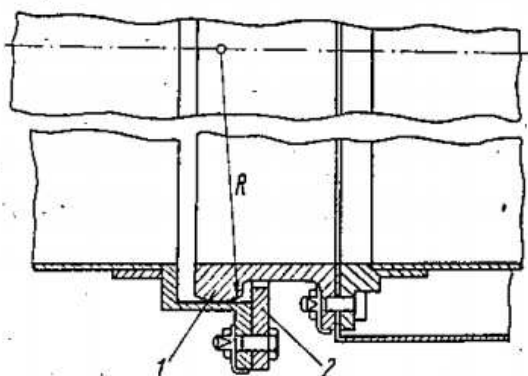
Schemat konstrukcyjny rury wylotowej silnika WK-1
